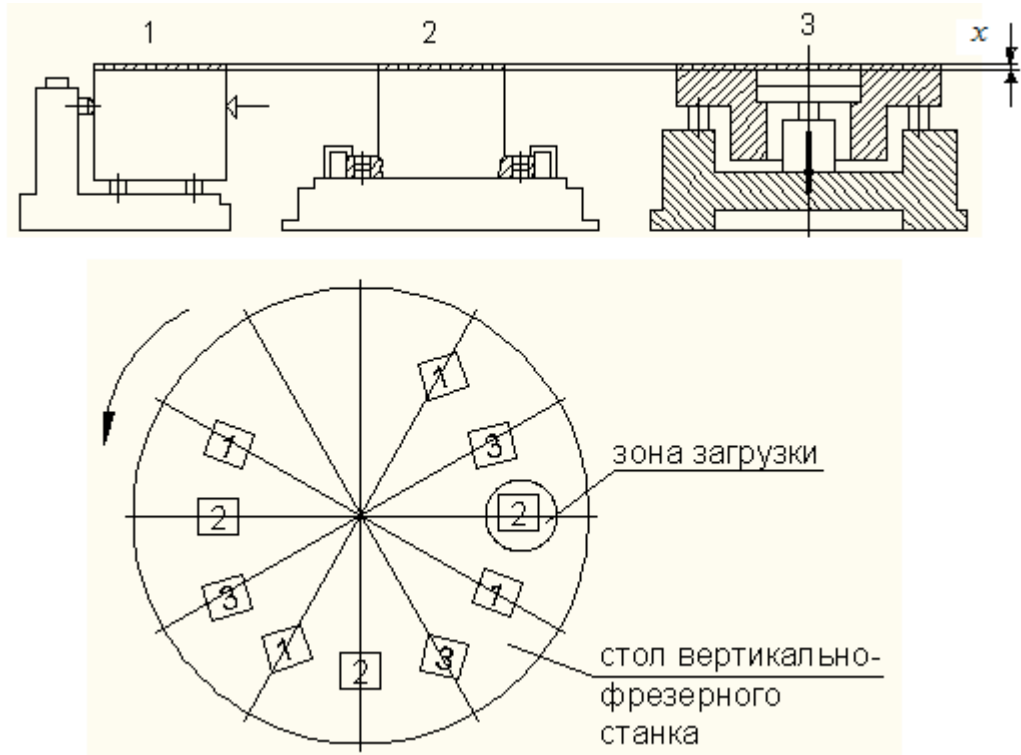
Комбинированное приспособление для групповой обработки.
